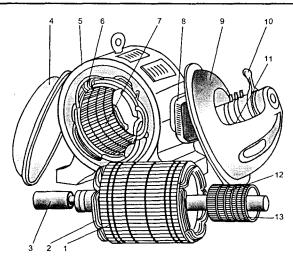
Асинхронный электродвигатель с фазным ротором: 1 — сердечник ротора; 2 — обмотка ротора; 3 — вал; 4 — подшипниковый щит со стороны привода; 5 — корпус статора; 6 — обмотка статора; 7 — сердечник статора; 8 — коробка выводов; 9 — подшипниковый щит со стороны контактных колец; 10 — рычаг короткозамыкающего приспособления; 11 — шеткодержатели внутри щита 9; 12 — контактные кольца; 13 — смещающееся вдоль вала кольцо короткозамыкающего приспособления
